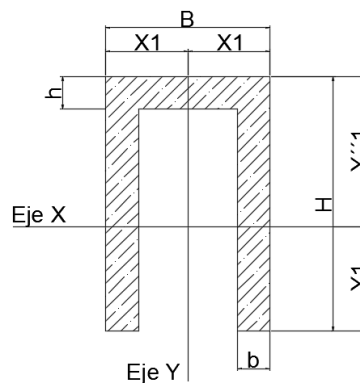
Parámetros de la viga para el cálculo de momento de inercia y desplazamiento. Fuente: Elaboración Propia
